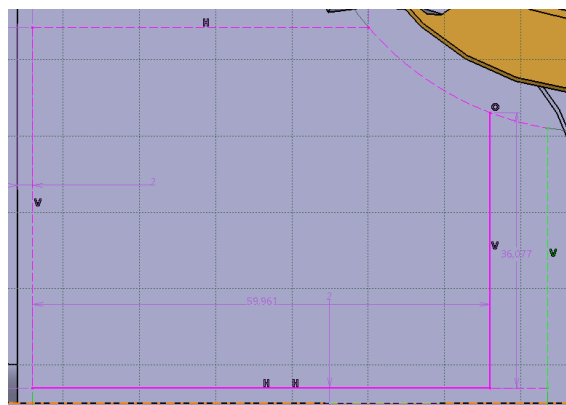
Proyección de la planta de la leva del embrague sobre la superficie disponible
